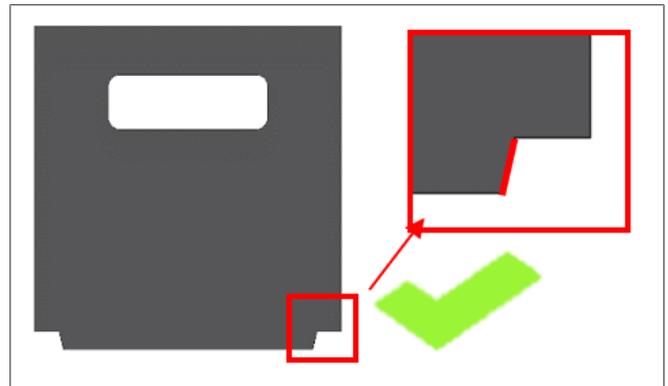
Getränke­kasten mit zu bevorzugender Einrastgeometrie
